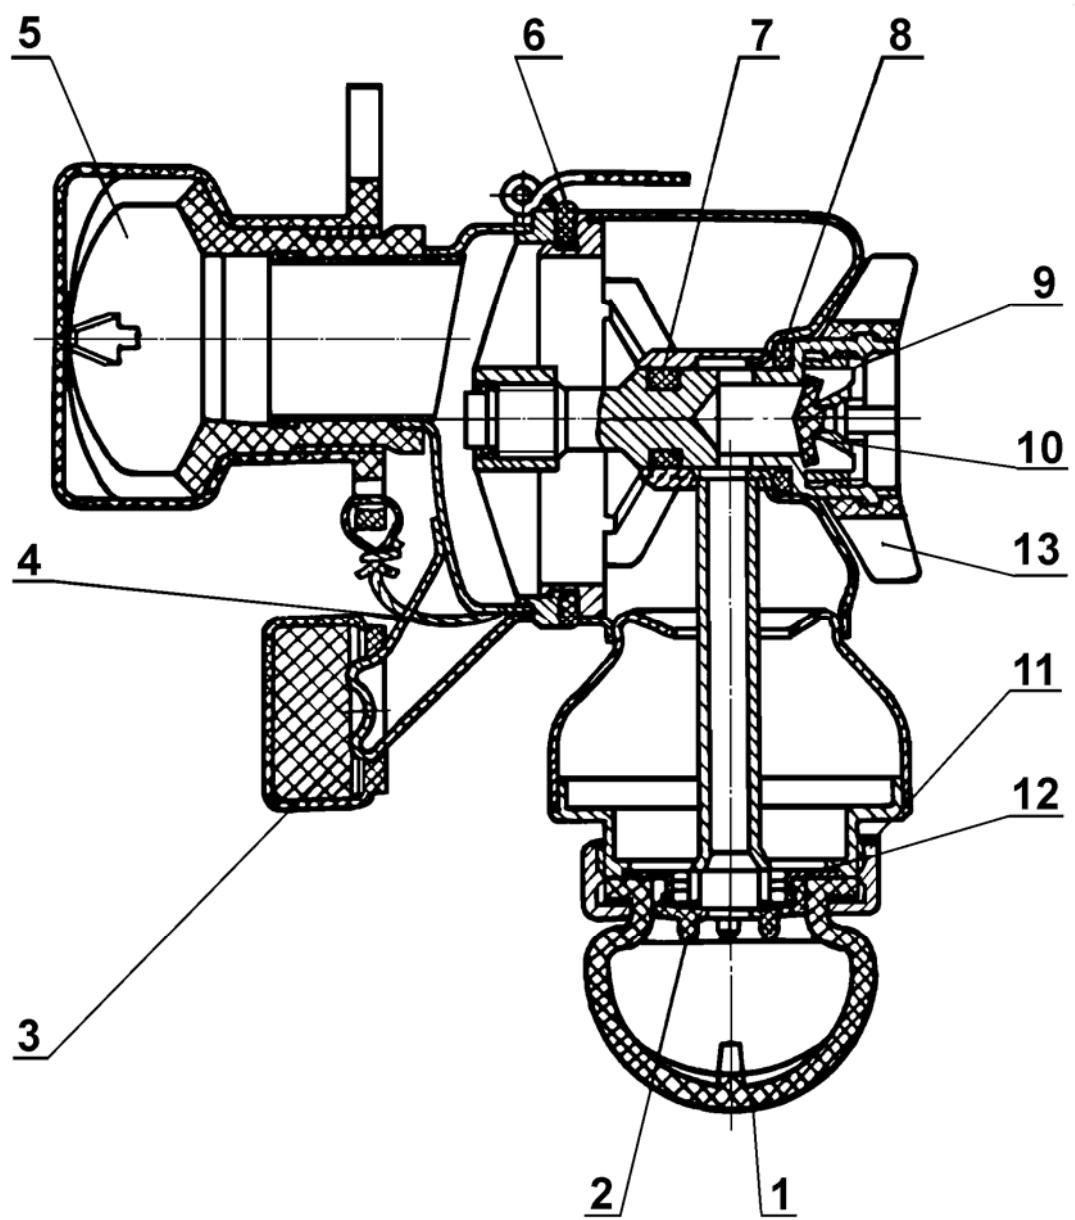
Часть лицевая (с мундштучным приспособлением)
